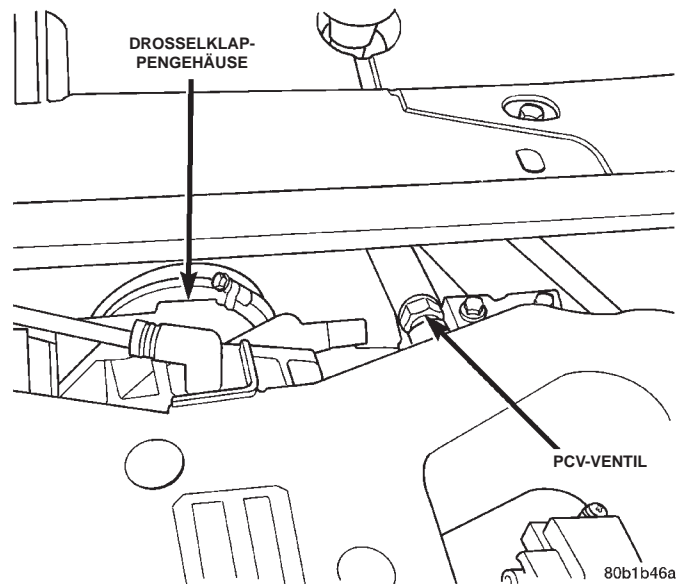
PCV-Ventil — 3.2L-/3.5L-Motor
